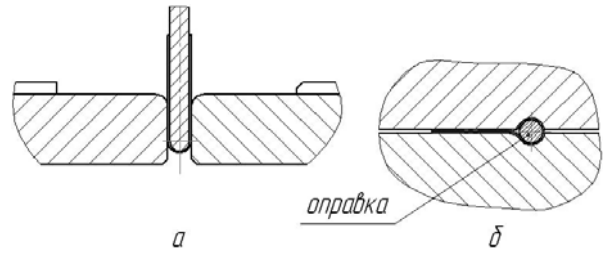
Переходы штамповки детали «шторка» гибкой на оправке:
